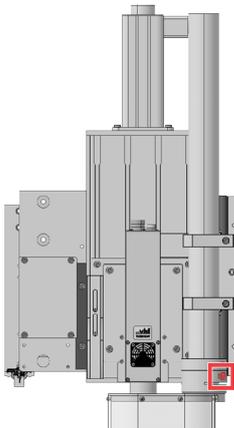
FESTZIEHEN DER SCHRAUBE DES EINGRIFFSCHUTZES
